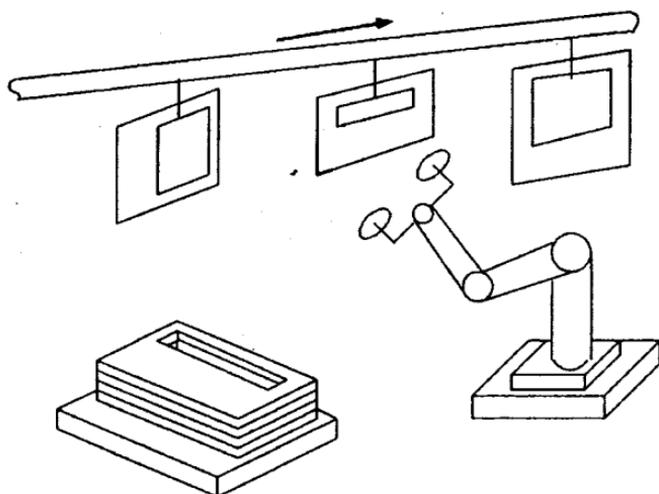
Адаптивный робот для съема и укладки деталей
